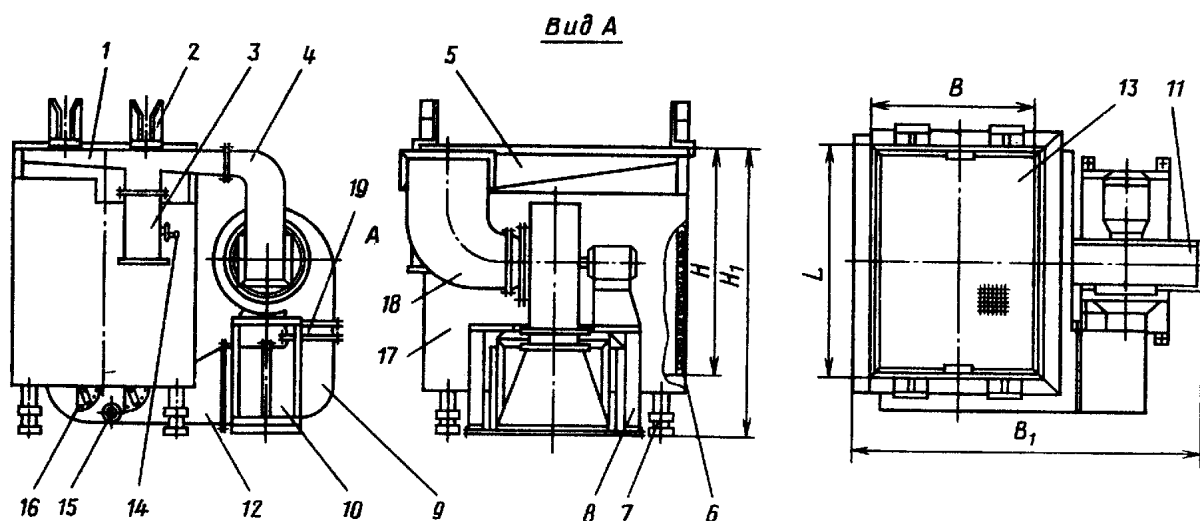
Камера для сушки деталей на подвесках: 1,4,5 – отсасывающие воздуховоды; 2 – опора; 3 – патрубок; 6 – теплоизоляция; 7 – регулируемая опора; 8 – рама вентиляторного агрегата; 9,12 – нагнетающие воздуховоды; 10 – электрокалорифер; 11 – вентиляторный агрегат; 13 – сетчатое дно; 14,16 – рукоятка шибера; 15 – термометр; 17 – корпус; 18,19 – брезентовые вставки
